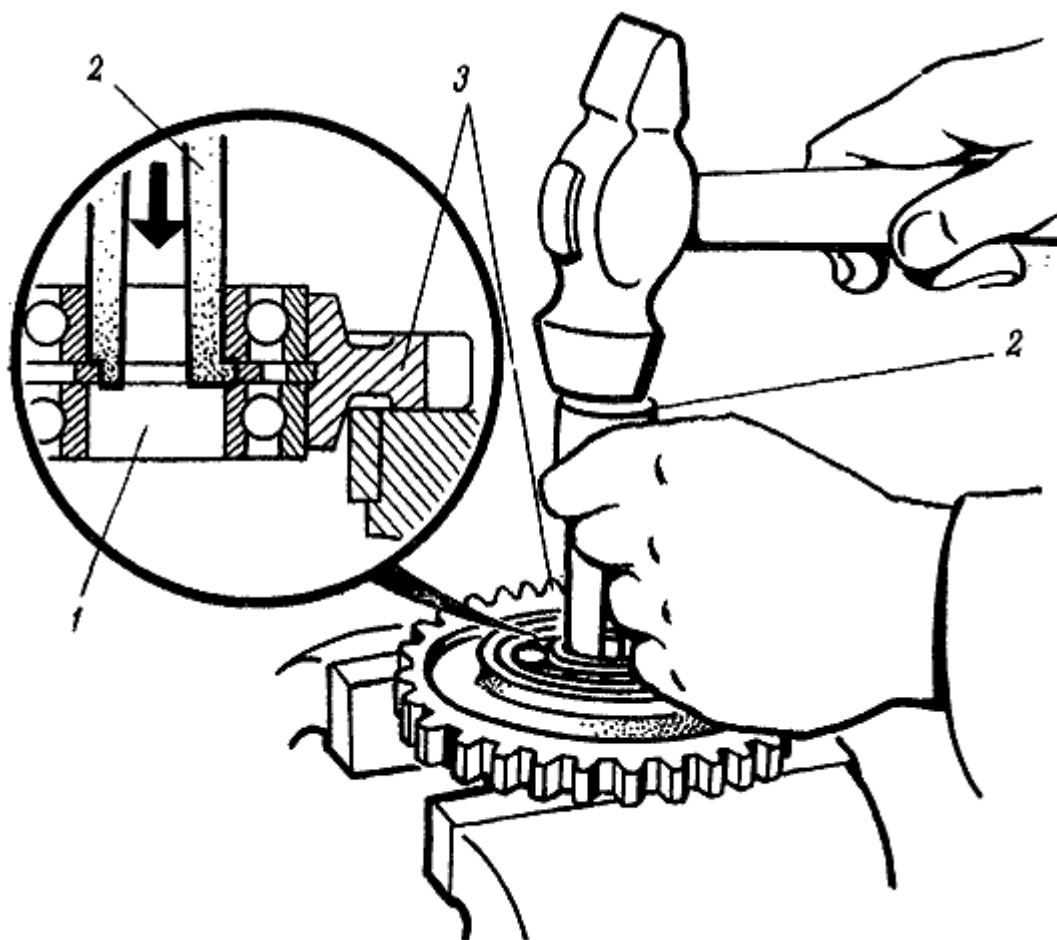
Выпрессовка подшипника из промежуточной шестерни привода гидронасоса:
